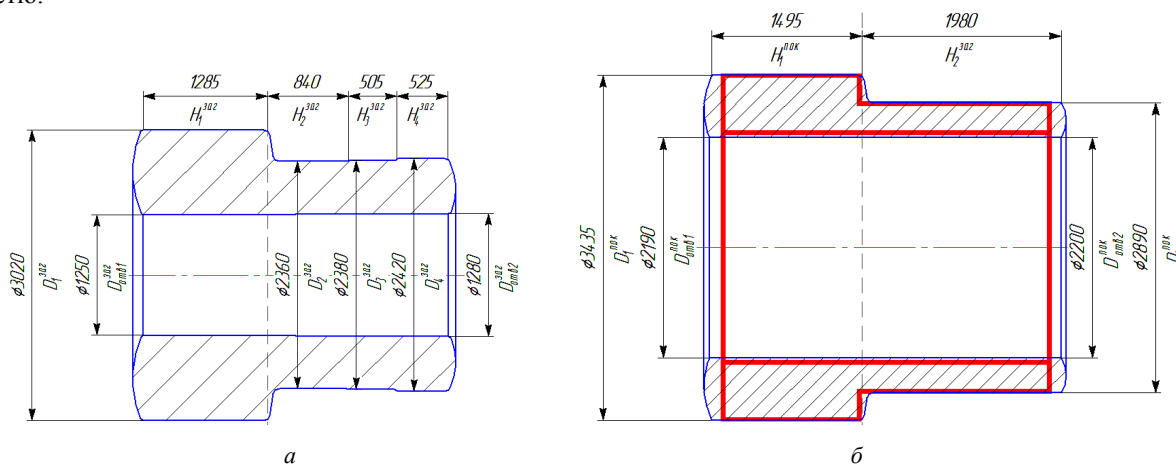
Заготовка (а) та поковка (б) отримана після розкочування
